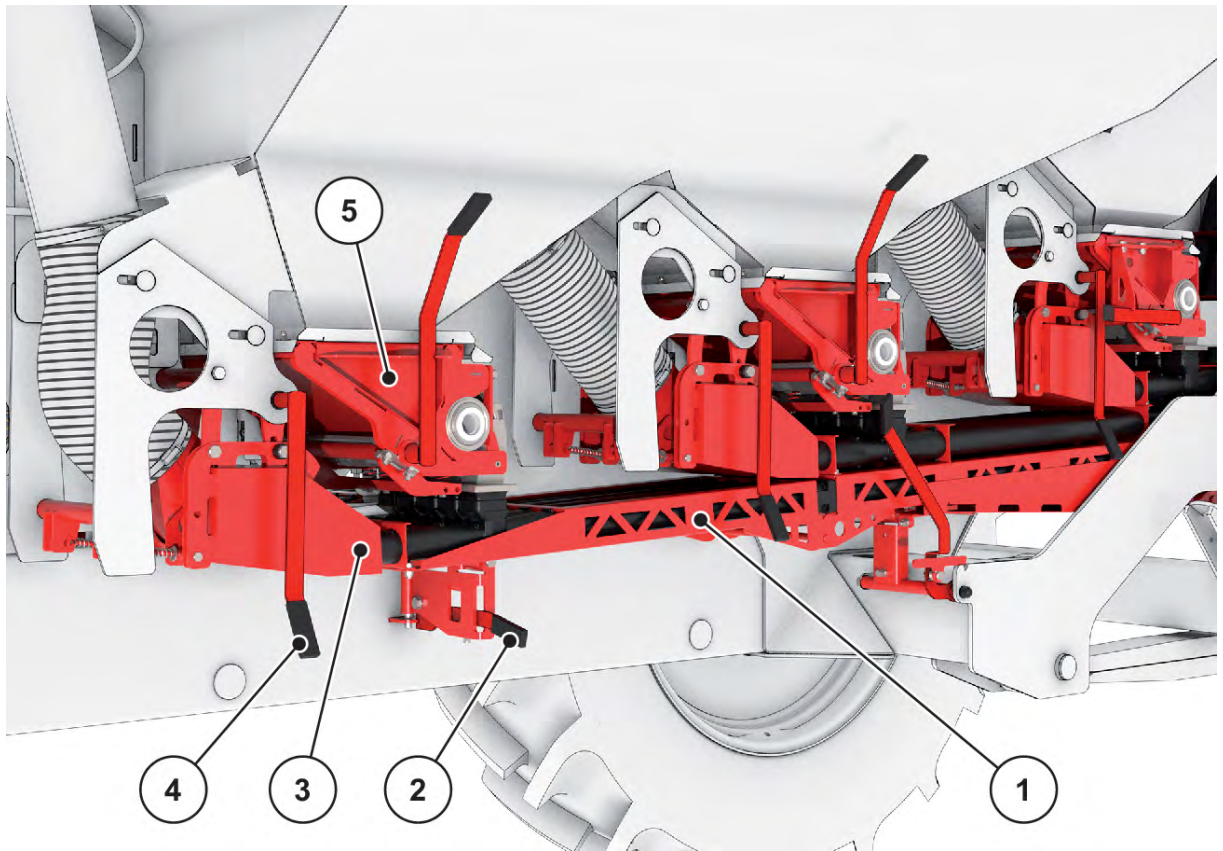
Maskinens komponentgrupper och funktion, detaljer sedda från höger sida
